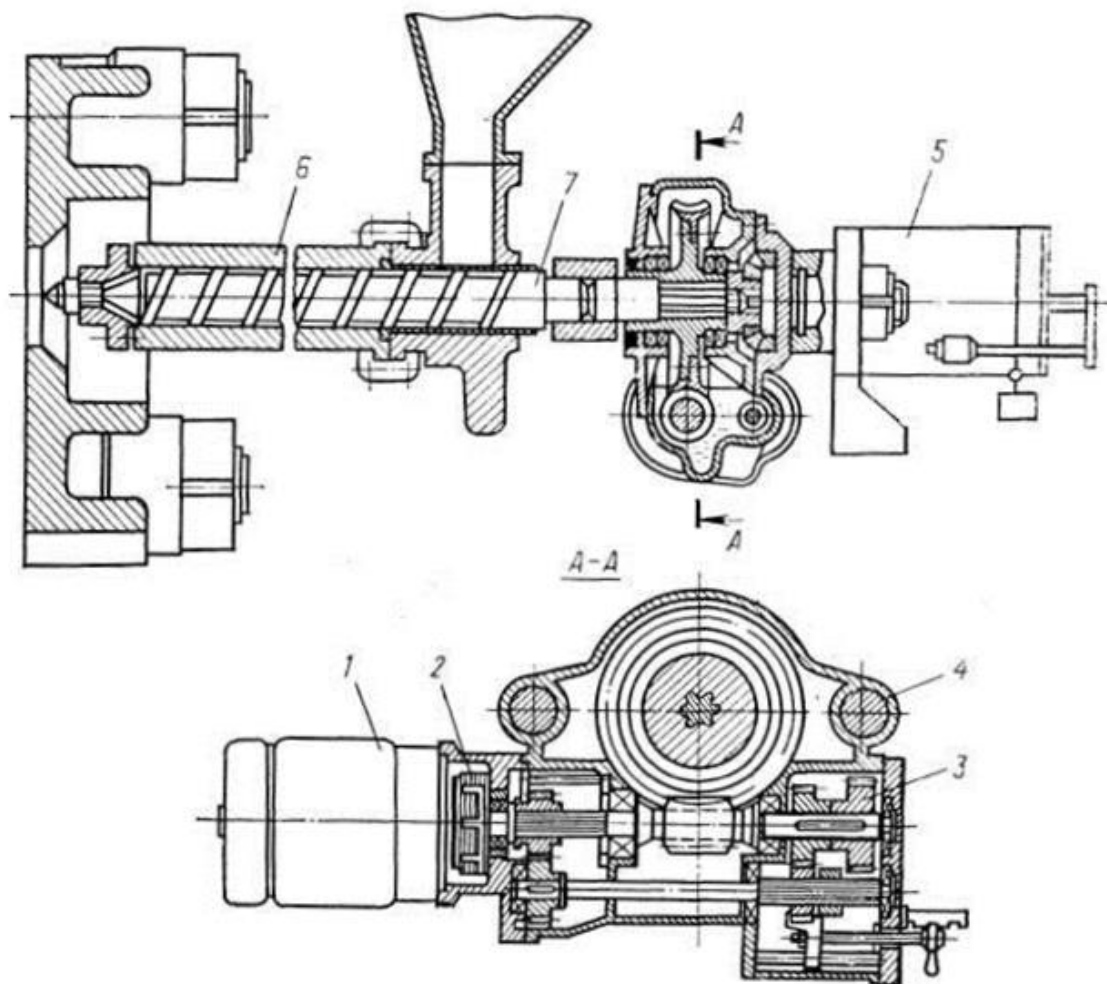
Черв'ячний механізм пластикації та упорскування з рухомим приводом:
